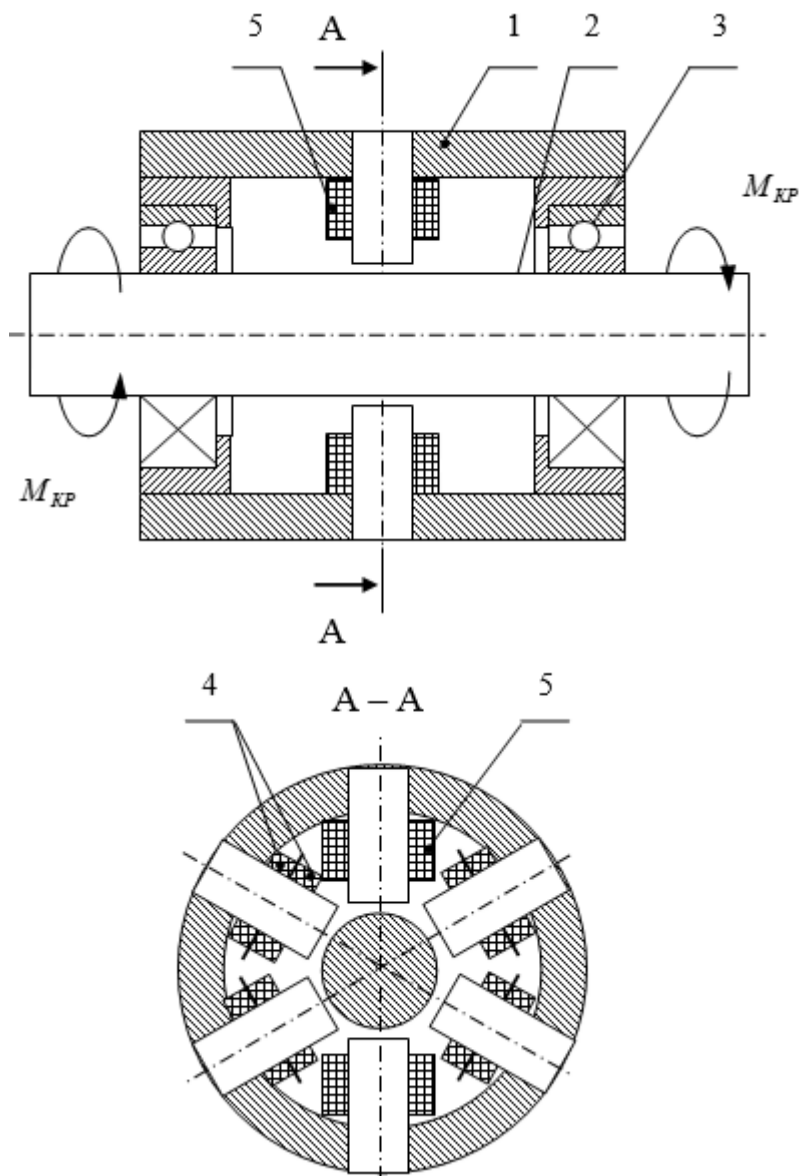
Схема устройства датчика крутящего момента: 1 – корпус датчика; 2 – вал; 3 – опорный подшипник; 4 – катушка измерительная; 5 – катушка возбуждения
